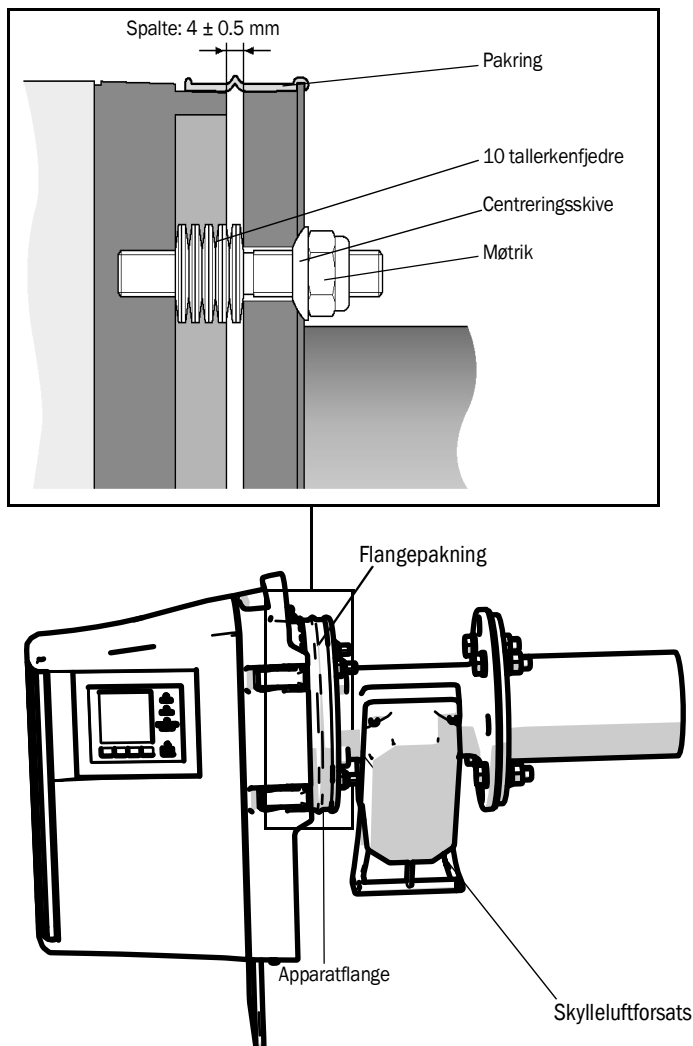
Skylleluftforsats monteret på "flange med rør"
